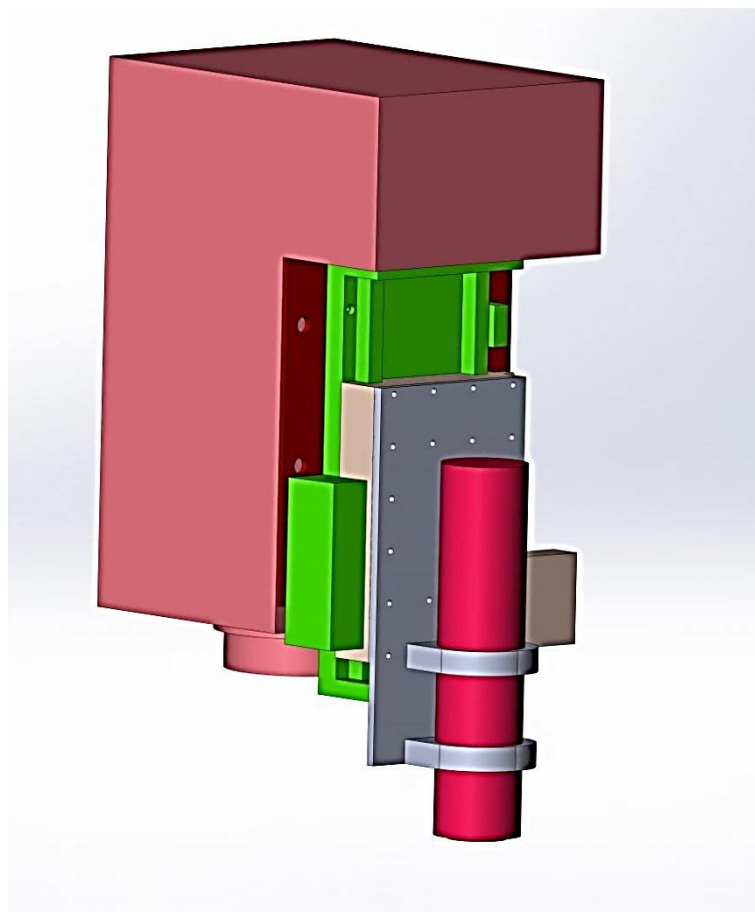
Вариант компоновки для цикла глубокого сверления
